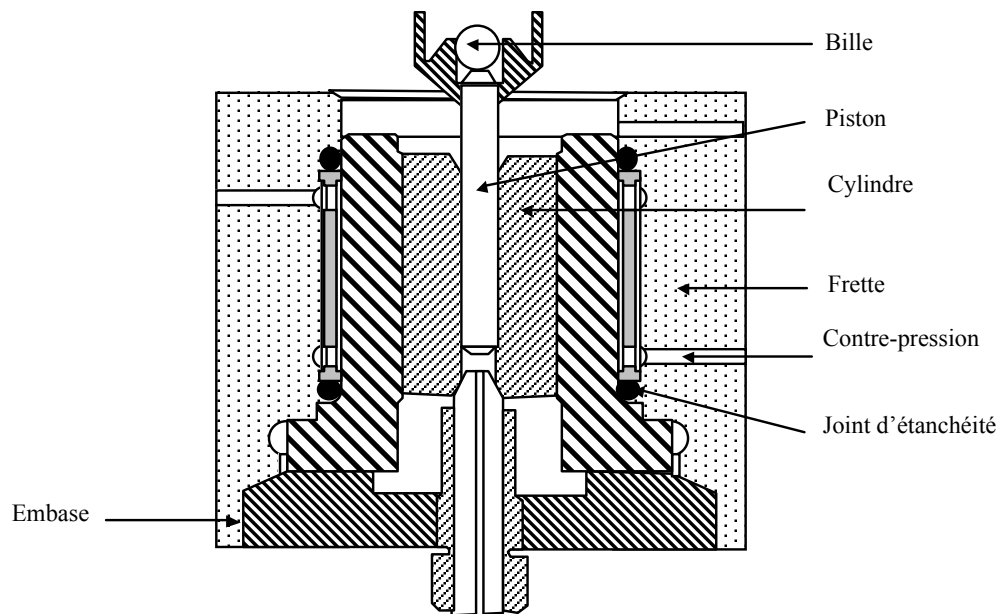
Schéma de l'ensemble piston-cylindre 1 GPa.
